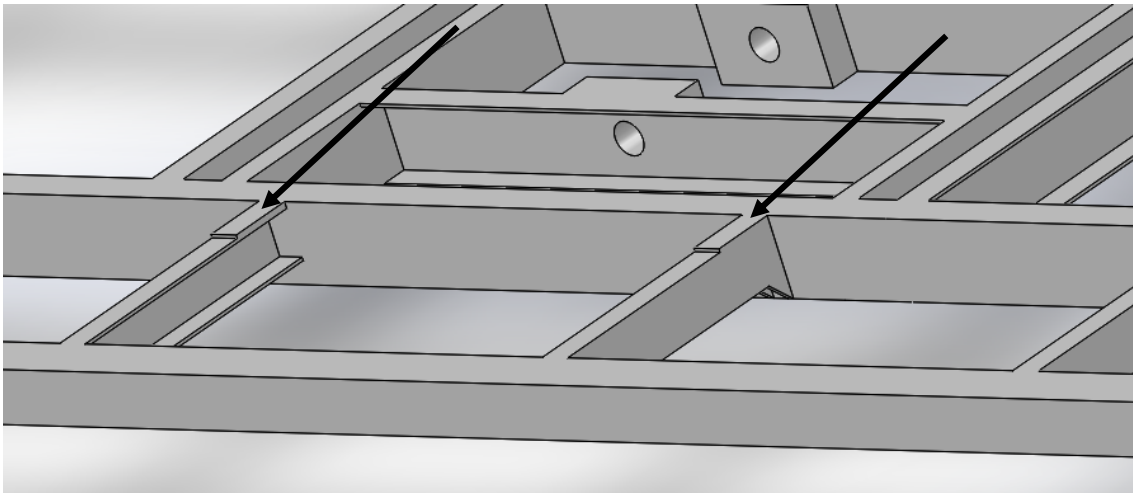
Pletinas de refuerzo en los travesaños exteriores.
